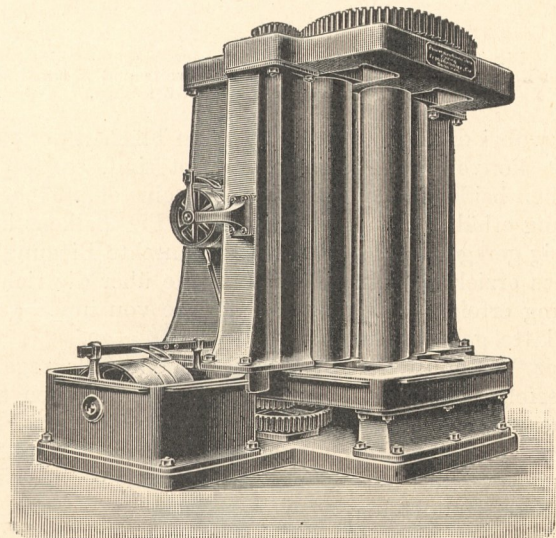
Stehende Vierwalzen-Blechbiegemaschine. Ausführung: Fr. Mönkemöller & Co., Bonn a. Rh.
